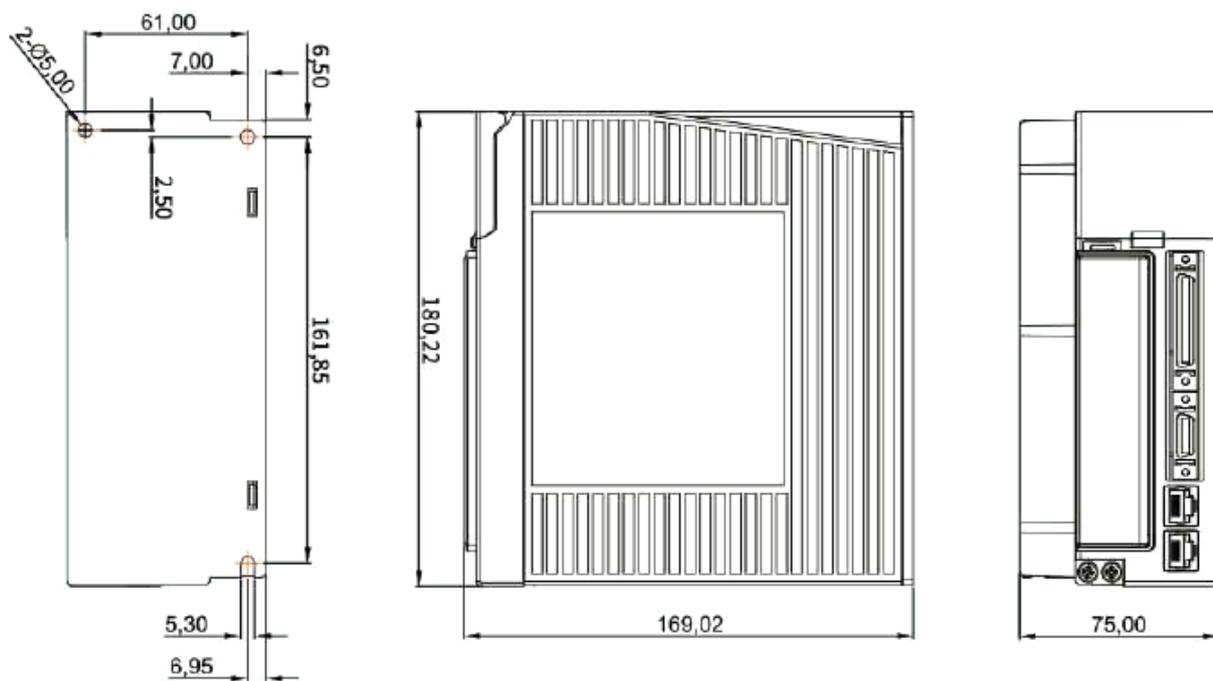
Габаритный чертеж серводрайверов LK-D2000.
